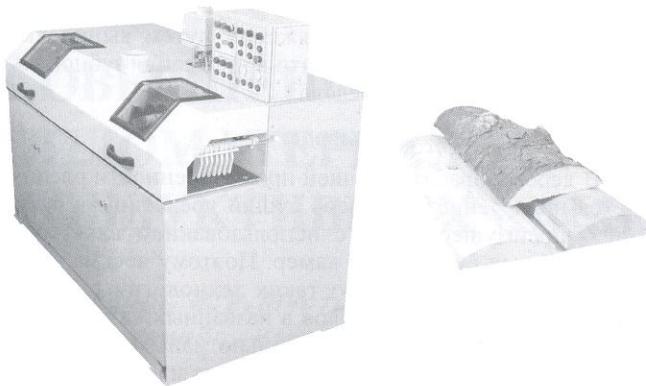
Фрезерно-пильный станок ПФП-100 для обработки горбыля (а), заготовка и готовое изделие (б)
